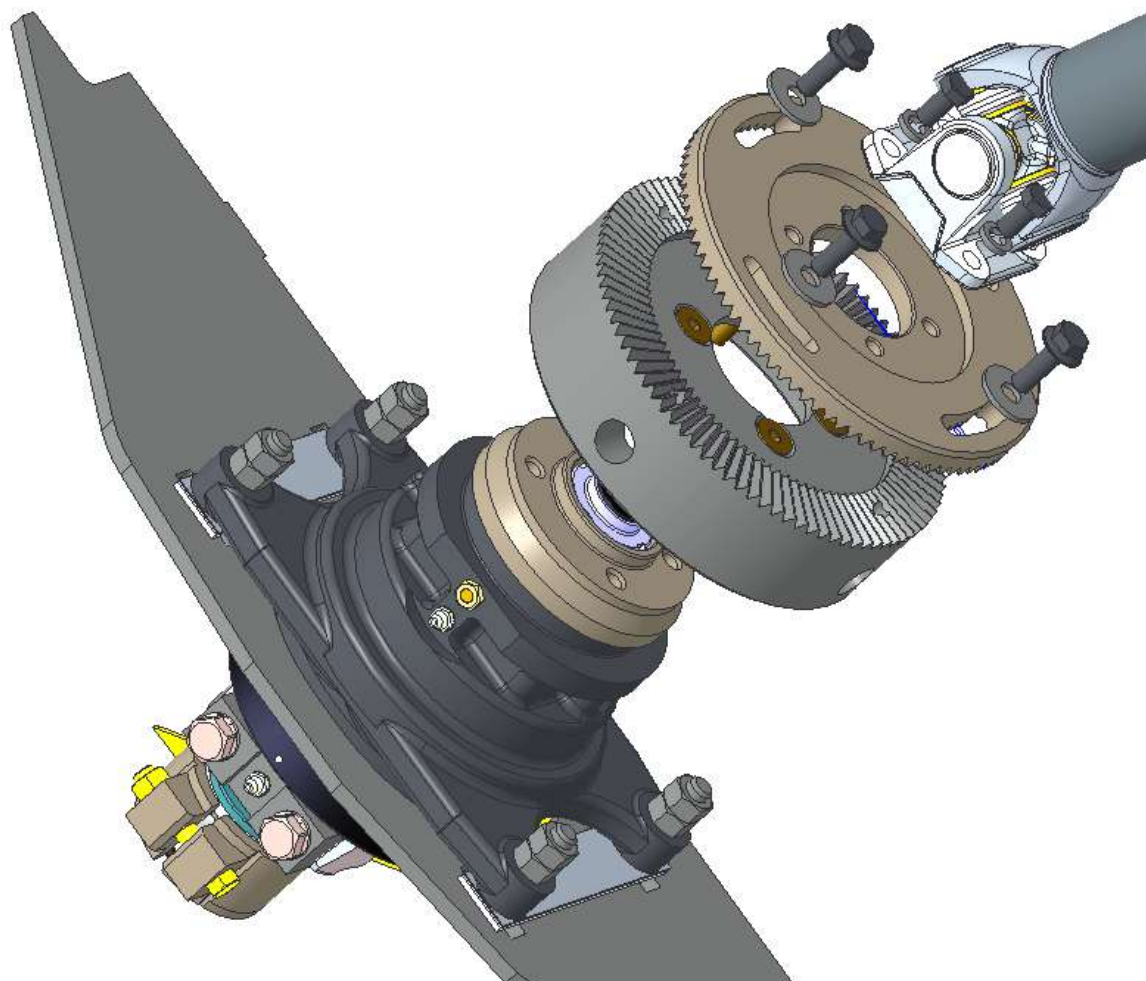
Схема разъемного маховика привода режущего аппарата.
